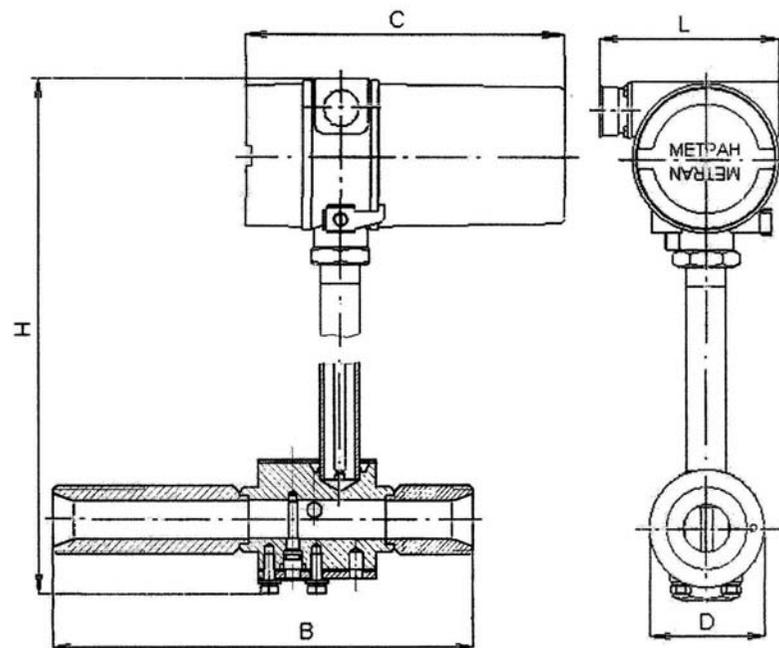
Габаритные и установочные размеры преобразователя исполнения В типоразмера Ду 25 мм.
